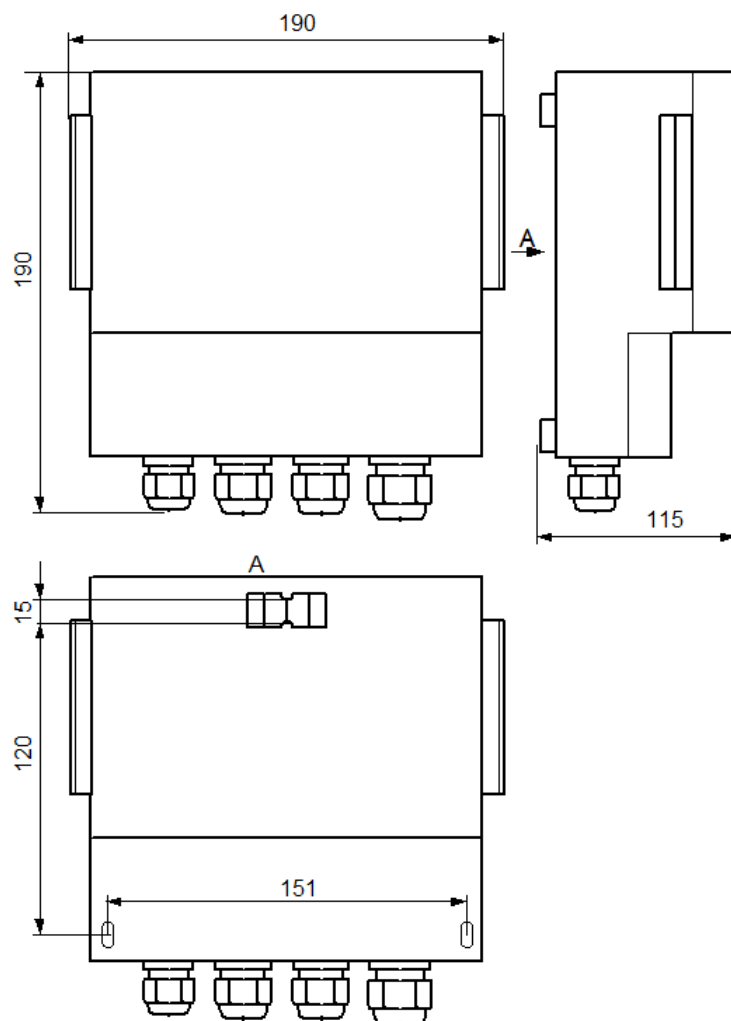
Габаритные и установочные размеры блока измерительного БИ-1-1
